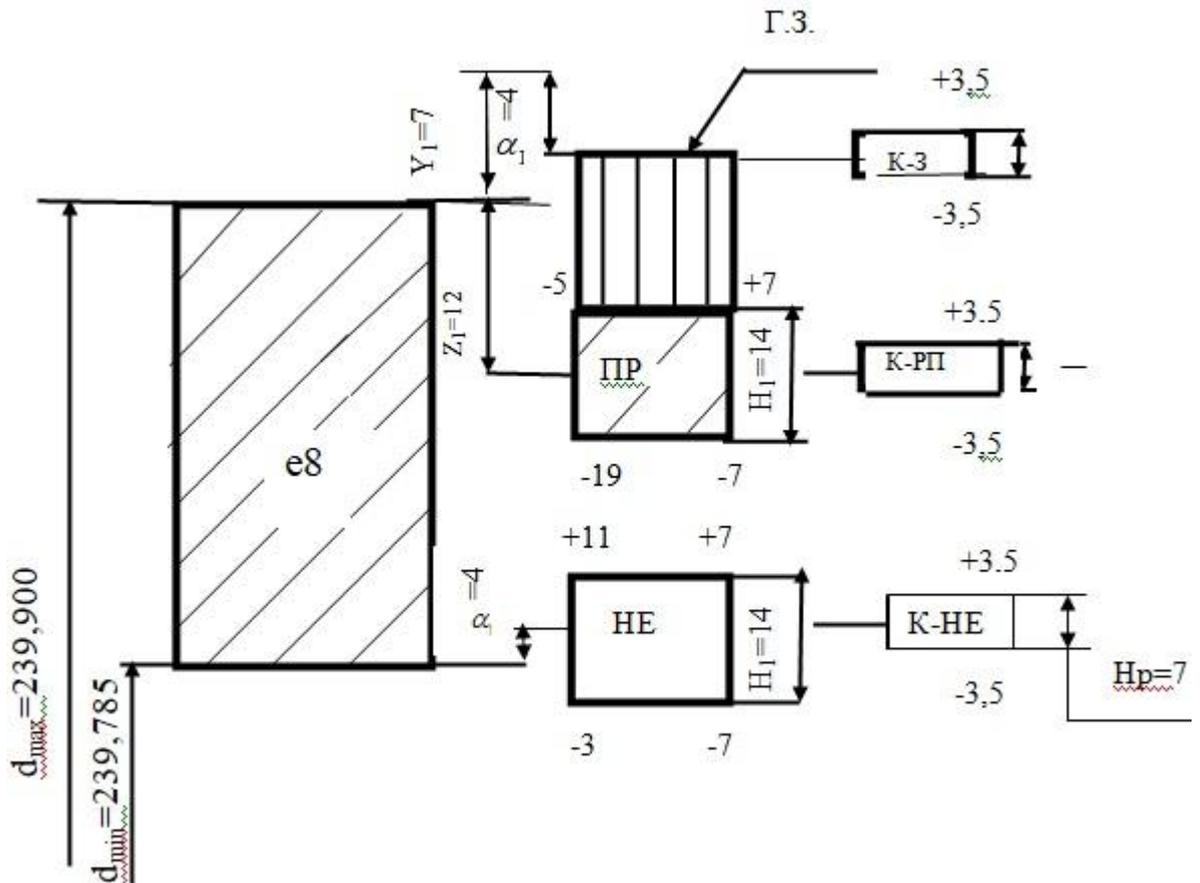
Схема розміщення полів допусків калібр-скоби для контролю вала $\varnothing 240e8_{(-0,215)}^{(-0,100)}$
